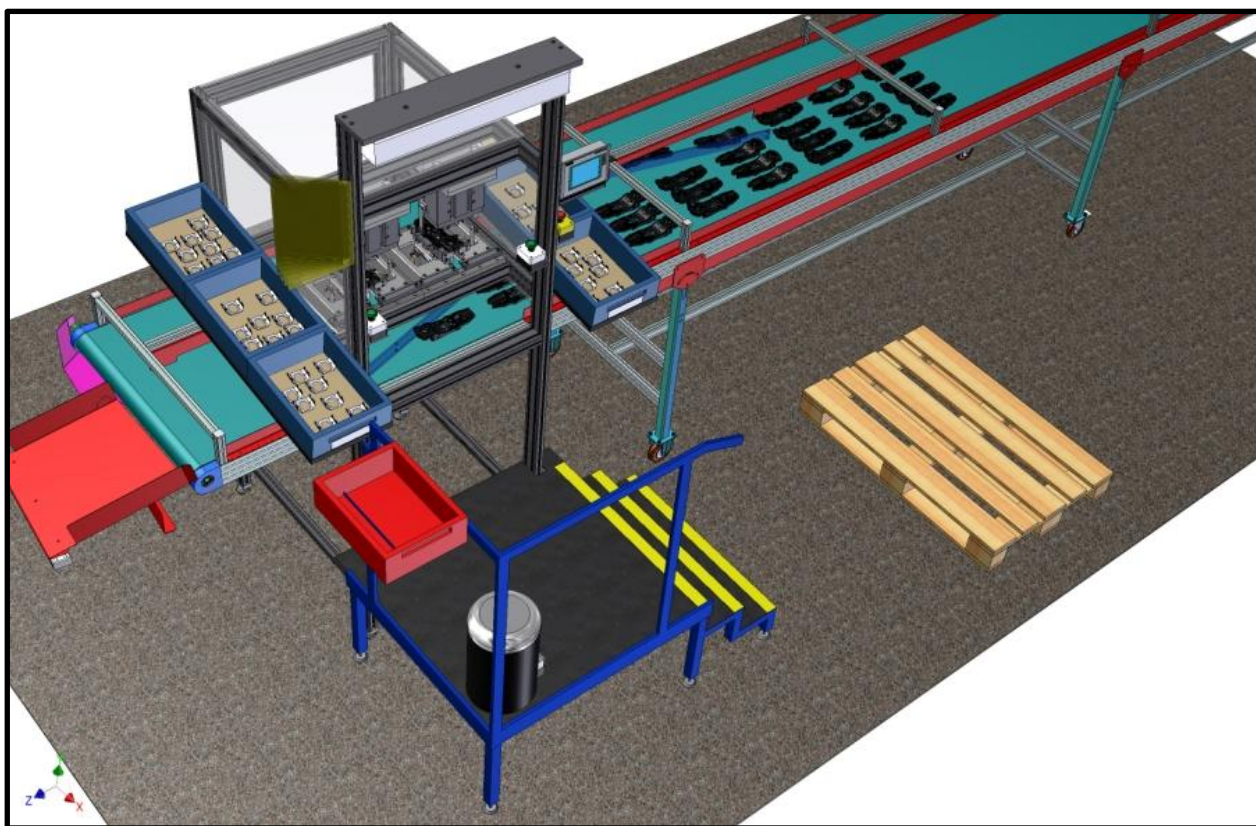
Konstrukce lisovacího stroje – Pohled 2
